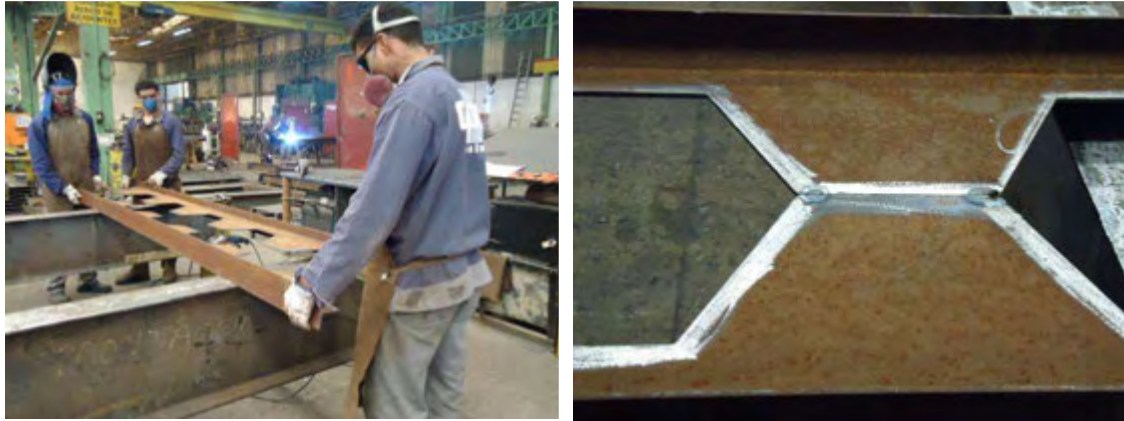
Posicionamento das metades e preparação do perímetro do corte (foto: Washington Vieira).
